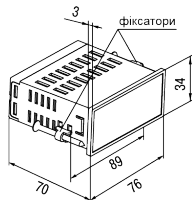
Габаритні розміри корпусу ЩЗ
